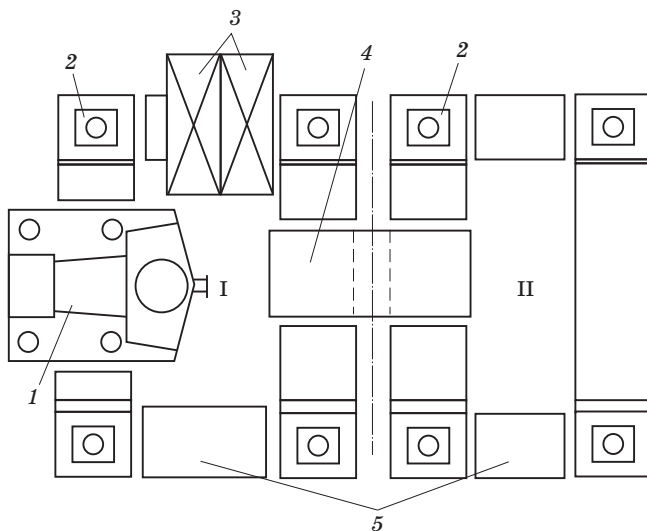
Схема автоматической линии для изготовления стержней по CO_2 -процессу
